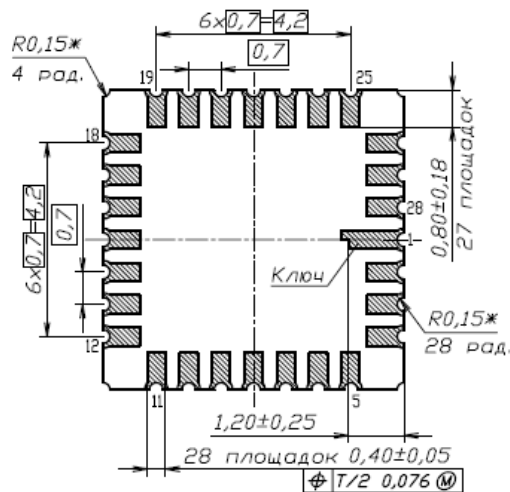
Габаритный чертеж корпуса МК 5123.28-1
